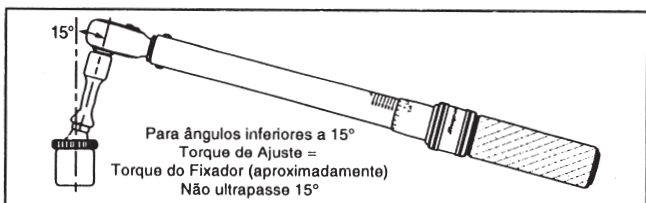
O torque do fixador é maior do que o torque do furo quadrado da chave dinamométrica.
